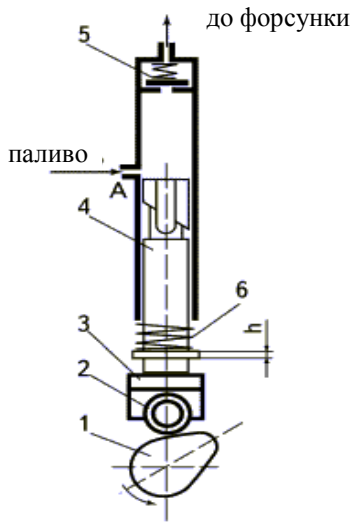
Схема паливного насоса: А – живильний канал; 1 – кулачок; 2 – ролик штовхача; 3 – штовхач; 4 – плунжер; 5 – пружина нагнітального клапана; 6 – поворотна пружина плунжера
